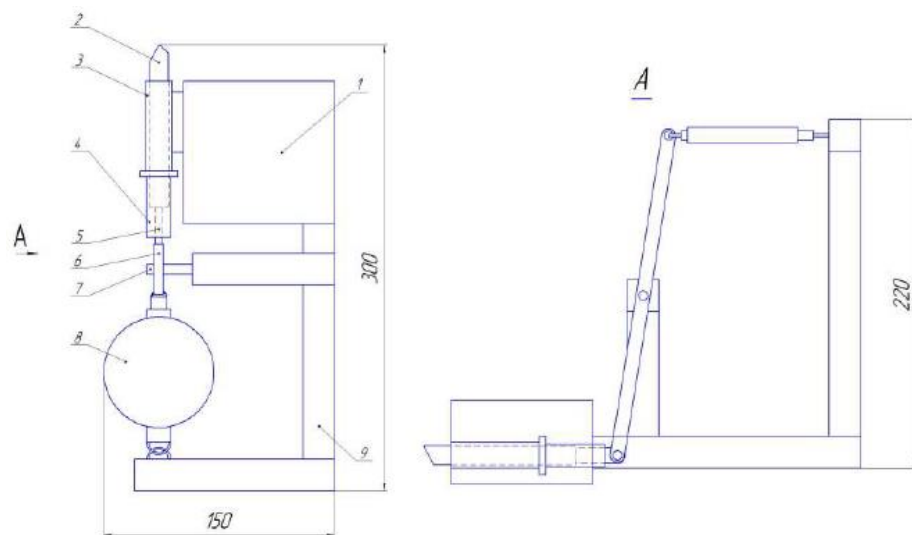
Схематичне зображення лабораторного обладнання для вимірювання радіальної складової сили різання R_y : 1 - тримач ножа машини; 2 - ріжучий елемент; 3 - напрямна ножа; 4 - тримач ножа; 5 - стрижень; 6 - коромисло; 7 - вісь коромисла; 8 - ваги ВБ-10; 9 - рамка.
